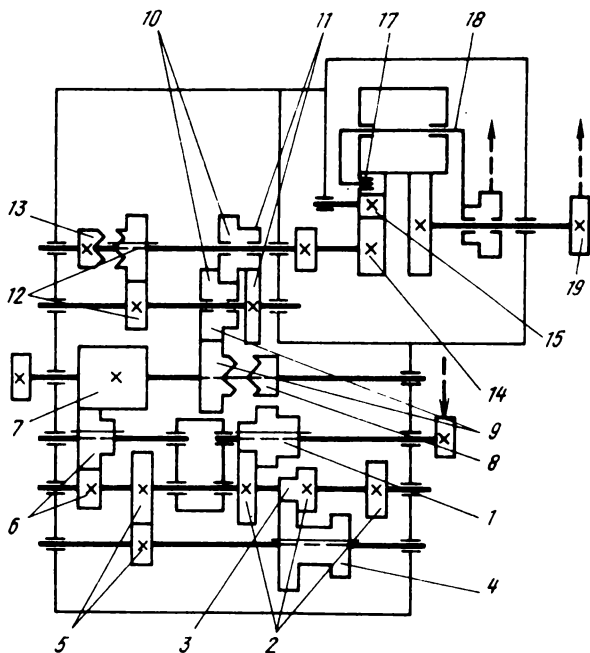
Кинематическая схема коробки подач станка ЛР-41
